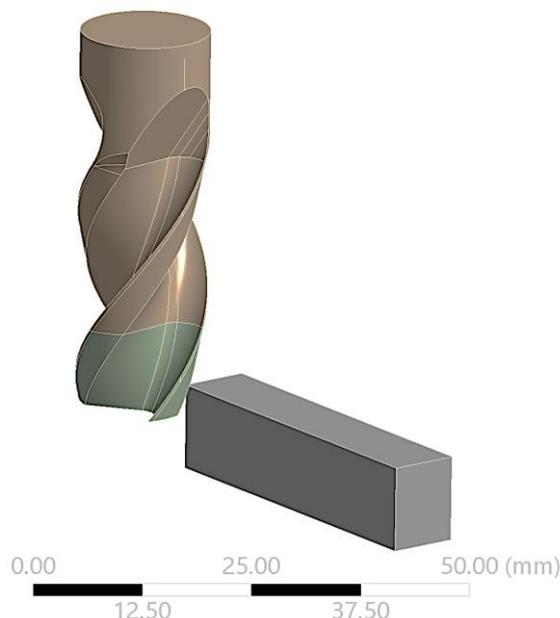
3D модель концевой фрезы с заготовкой
